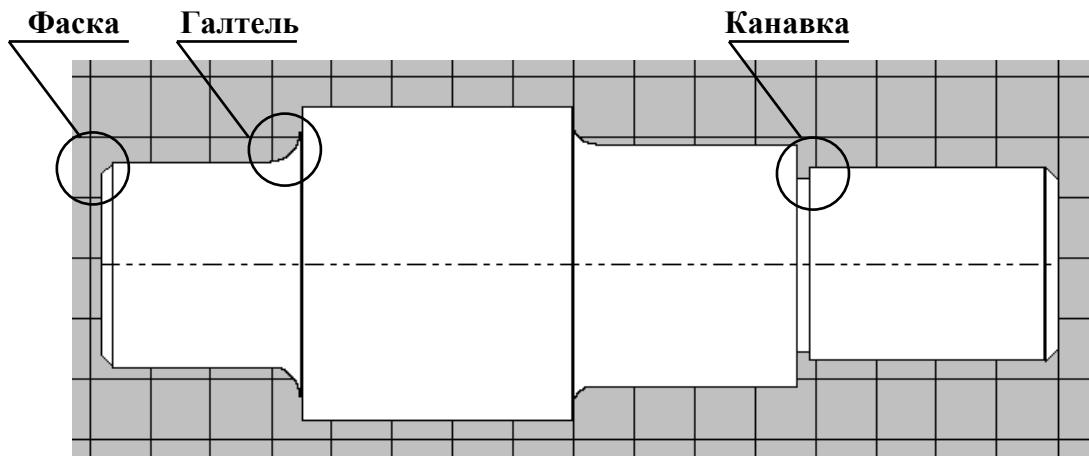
Редактор APM Shaft. Фрагмент вала с фасками, галтелями и канавкой
